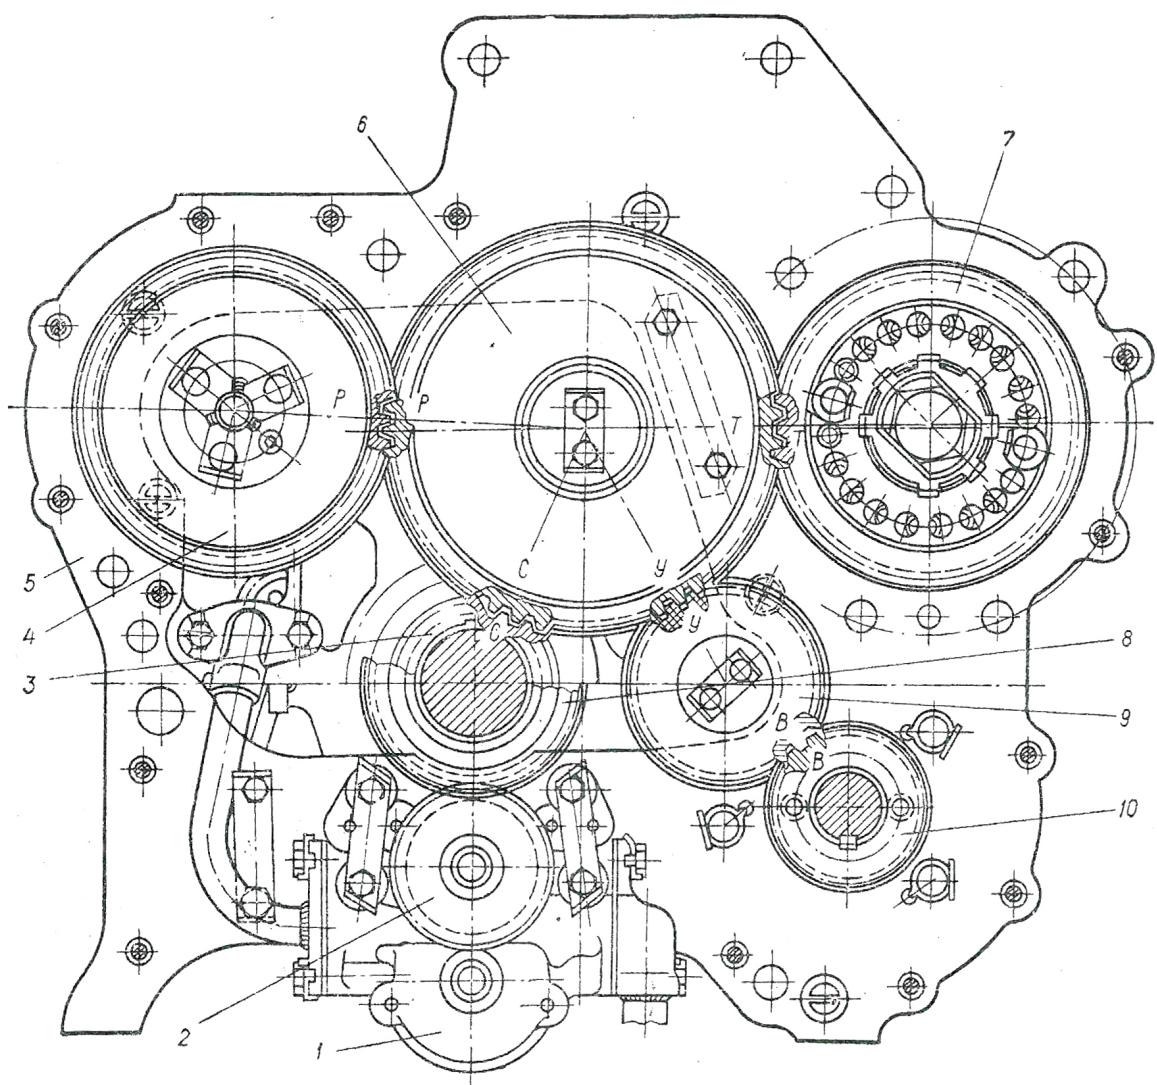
Установка шестерни газораспределения и привода вспомогательных механизмов:
